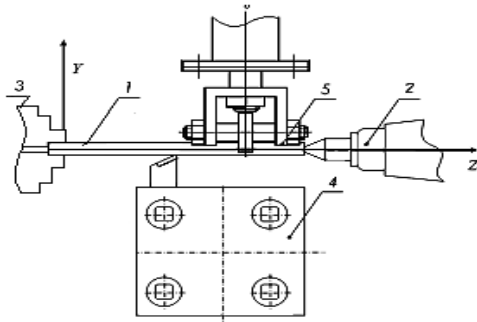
Схема обработки заготовки с компенсирующим усилием: 1 – нежесткая заготовка ($L = 200$ мм, $d_3 = \text{Ø}14$ мм); 2, 3 – центры; 4 – суппорт с резцом проходным отогнутым; 5 – компенсатор
